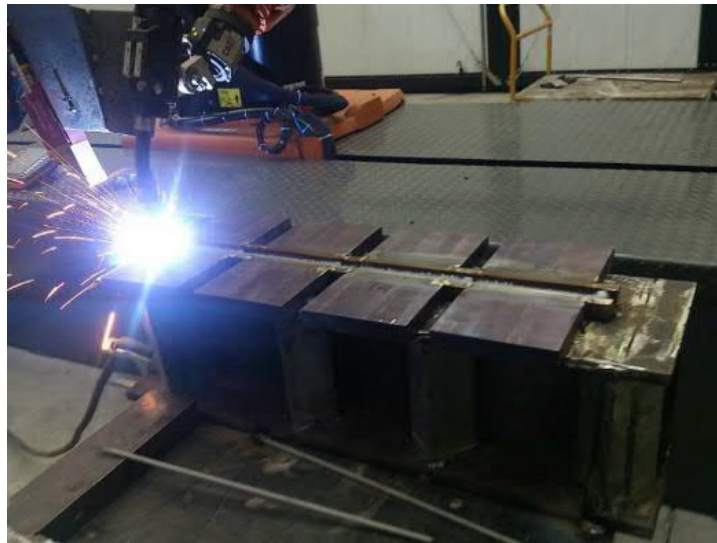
Soldadura GMAW robotizada, placas de 250x130x22 mm.
